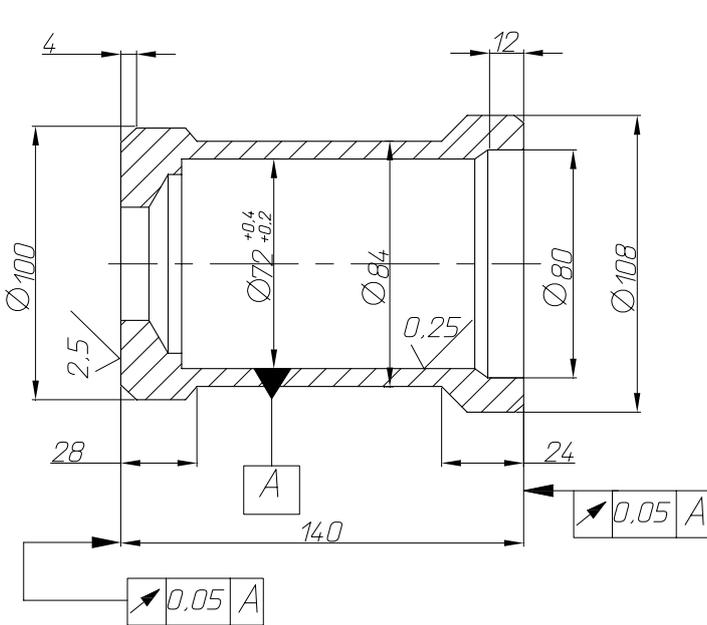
Конструктивные размеры деталей подставки для спрессовки шестерён промежуточного вала
